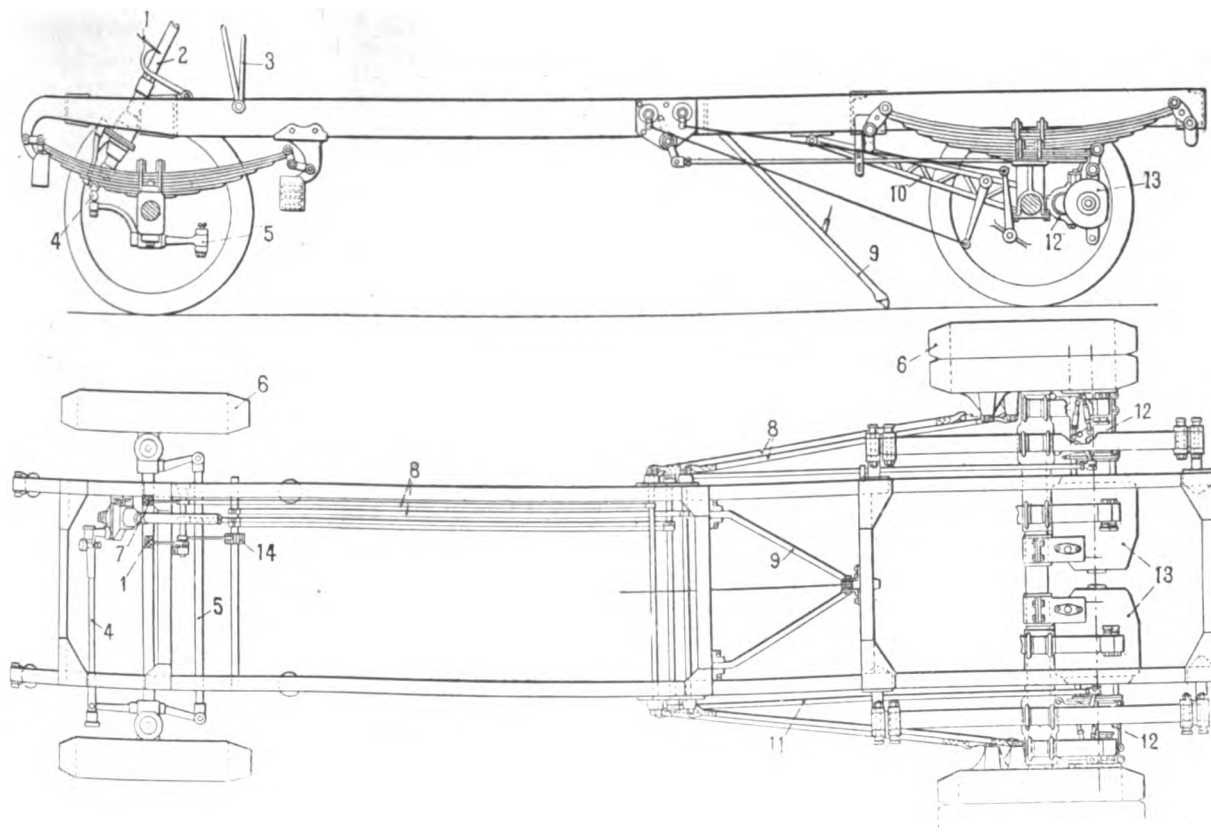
Vues en élévation et en plan du camion électrique Laporte (n° 12).
